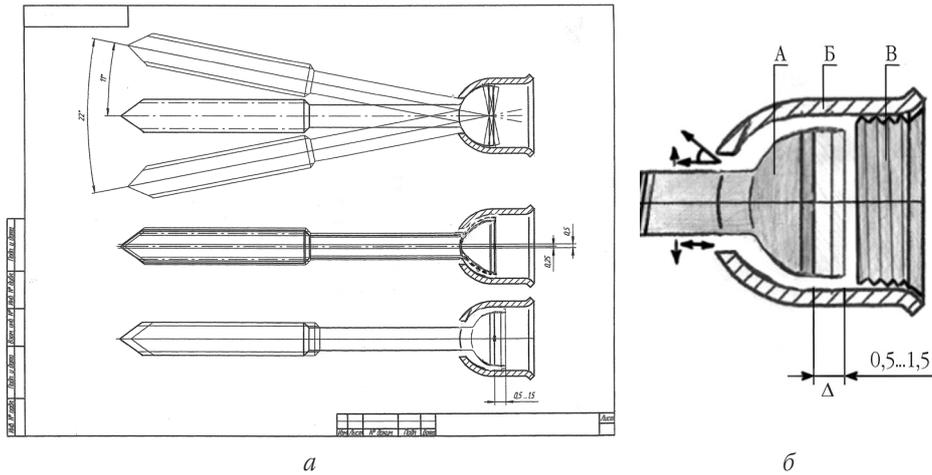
Динамический фиксатор: а — схема движений в устройстве; б — рабочая пара “чашка — винт”
